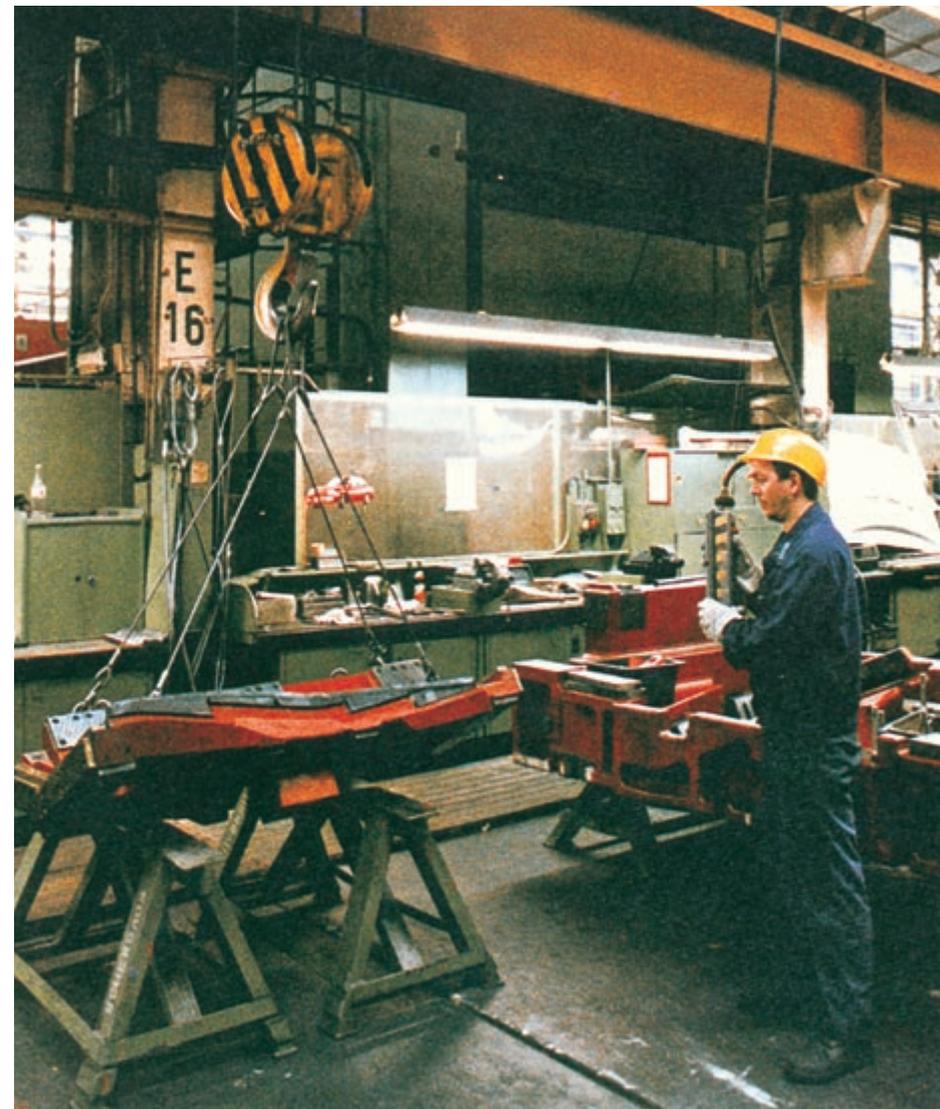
Der Kranführer steuert den Kran mittels der an der Kranbrücke hängenden Steuertafel
